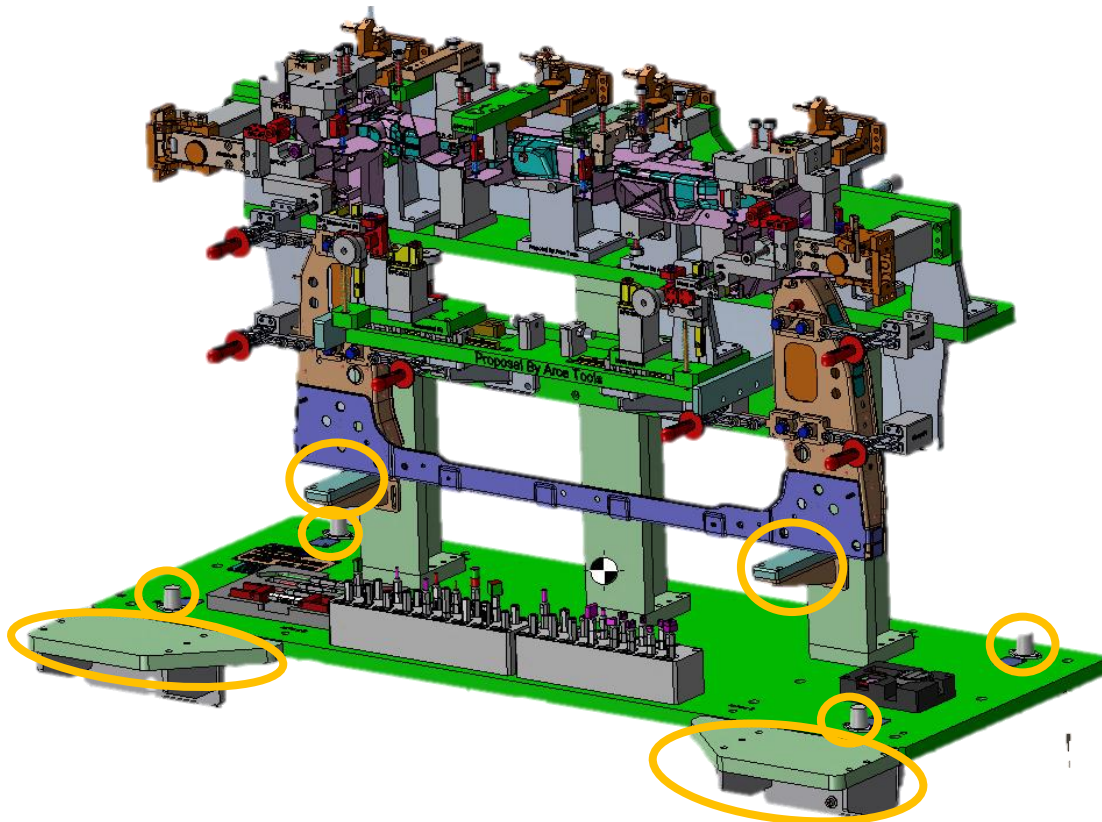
DISEÑO FINAL DEL DISPOSITIVO.
